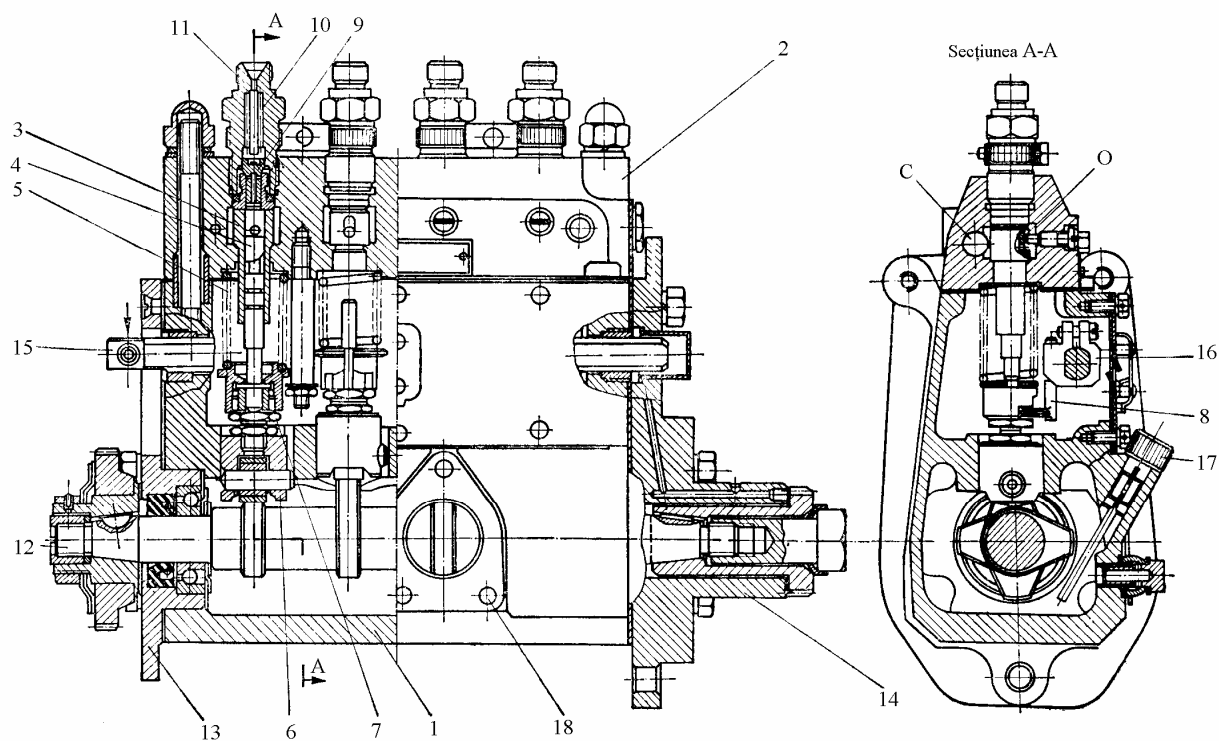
Pompa de injecție cu piston sertar: 1- corp pompă; 2- capac pompă; 3- cilindru; 4- piston sertar; 5- arc; 6- împingător cu rolă; 7- șurub reglaj; 8- manșon; 9- supapă refulare; 10- arc; 11- racord înaltă presiune; 12- ax cu came; 13,14- flanșe; 15- tijă reglare; 16- colier; 17- nivelă; 18- șurub; C- canal; O- orificiu
